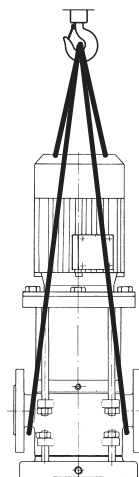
Hebezeug befestigen an Blockpumpe (vertikale Ausführung)
